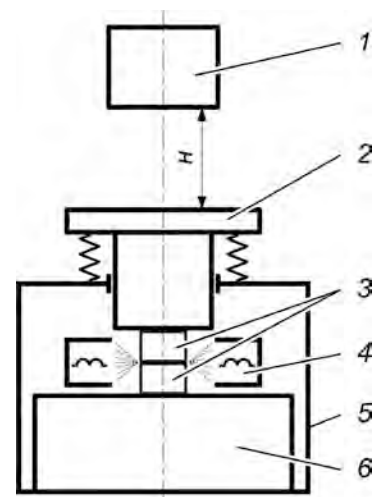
Схема установки для ударной сварки в вакууме: 1 — ударник; 2 — ходовой шток; 3 — свариваемые детали; 4 — нагреватель; 5 — сварочная вакуумная камера; 6 — массивная опора
